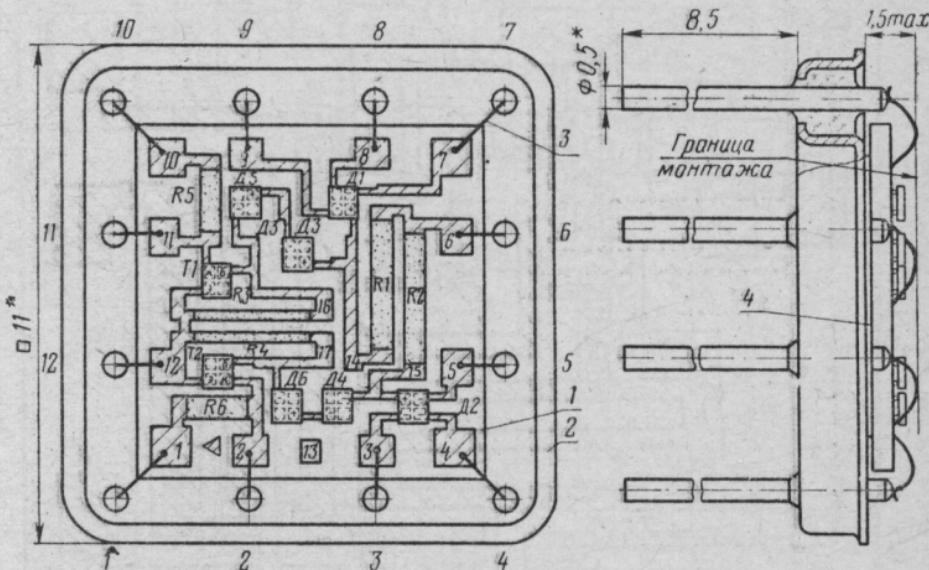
Сборочный чертеж гибридной тонкопленочной микросхемы.
